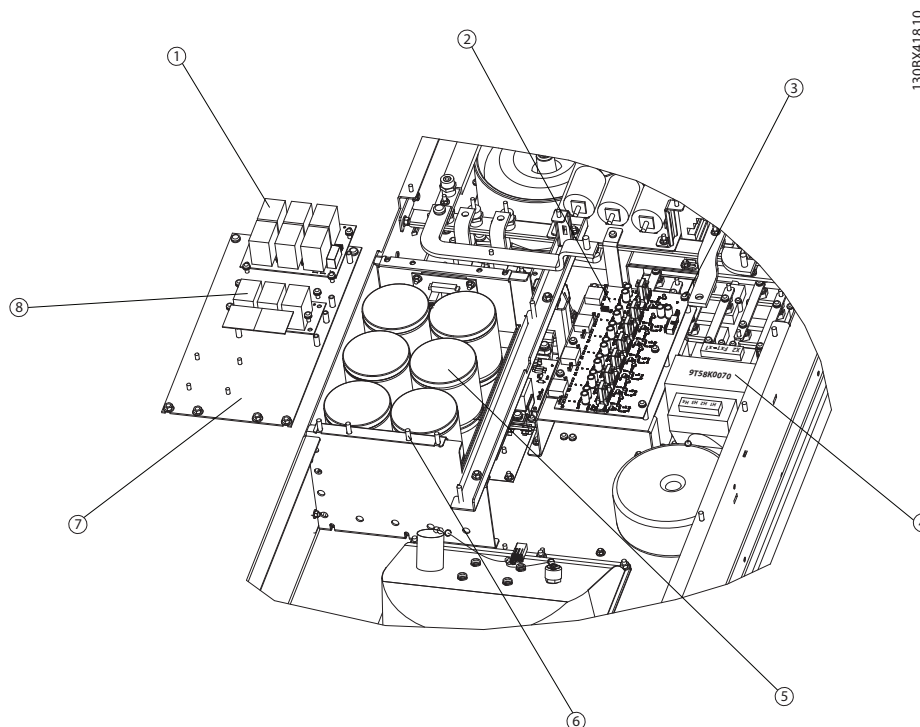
Placa de Montagem do Terminal de Entrada
